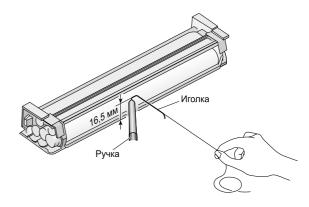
Регулировка положения главного полюса магнитного ролика в блоке проявителя
